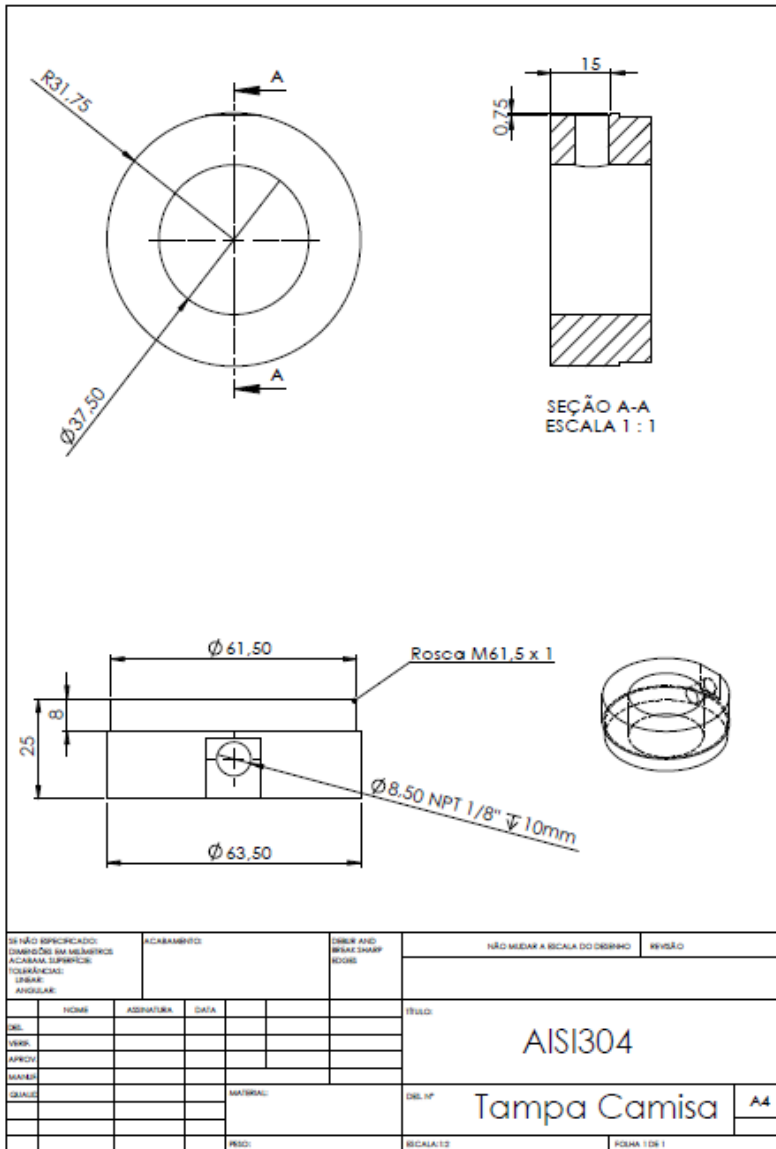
Figura IX: Vista da camisa/cilindro de aquecimento da coluna
